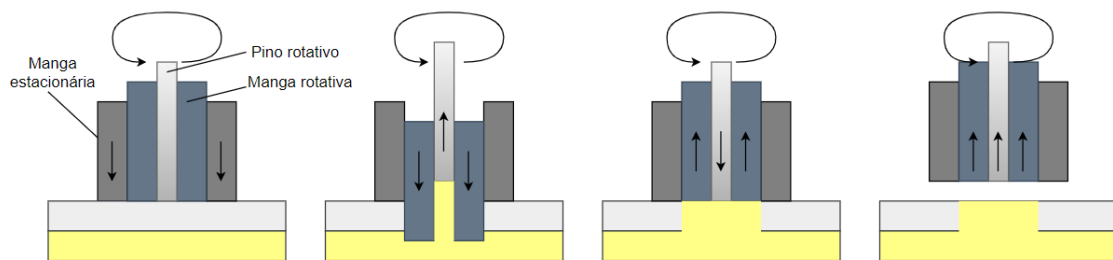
Soldadura por fricção. Adaptado de [41]
